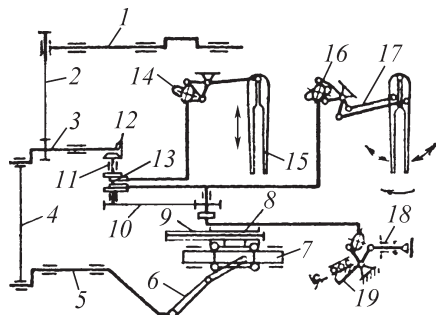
Кинематическая схема переключника для ГKM с вертикальным разъемом матриц: 1 — главный вал; 2 — цепная передача; 3 — распределительный вал; 4 — кривошипно-шатунный механизм; 5 — промежуточный вал; 6 — двуплечий рычаг; 7 — каретка; 8 — труба; 9 — пружина; 10 — цепная передача; 11 — кулачковый вал; 12 — шестеренная передача; 13 — система кулаков; 14 — кулак привода подъема и опускания клещей; 15 — клещи; 16 — кулак привода сжатия клещей; 17 — рычаги сжатия клещей; 18 — возвратная пружина; 19 — рычаг
